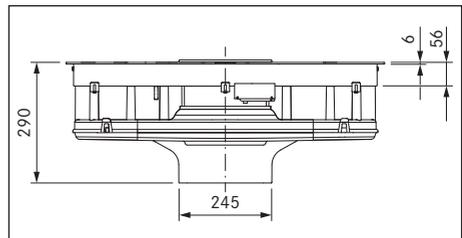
BHA dimensioni apparecchio vista frontale
